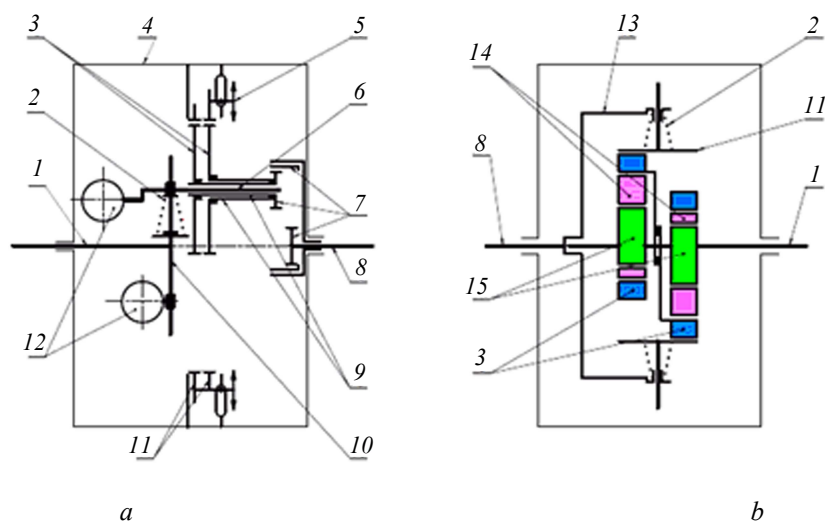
Перспективные модификации планетарной плавнорегулируемой передачи: а – с соосными зубчатыми венцами сателлита; б – оппозитными зубчатыми венцами сателлита; 1 – ведущий вал; 2 – пружина силового замыкания сателлита и секторов центрального зубчатого колеса; 3 – двухпоточный сателлит; 4 – корпус передачи; 5 – механизм регулирования передаточного отношения; 6 – кривошип; 7 – вспомогательная планетарная передача; 8 – ведомый вал; 9 – торсион; 10 – направляющая; 11 – сектора центрального зубчатого колеса; 12 – противовес; 13 – корпус центрального зубчатого колеса; 14 – эксцентричные втулки; 15 – эксцентрики ведущего вала
